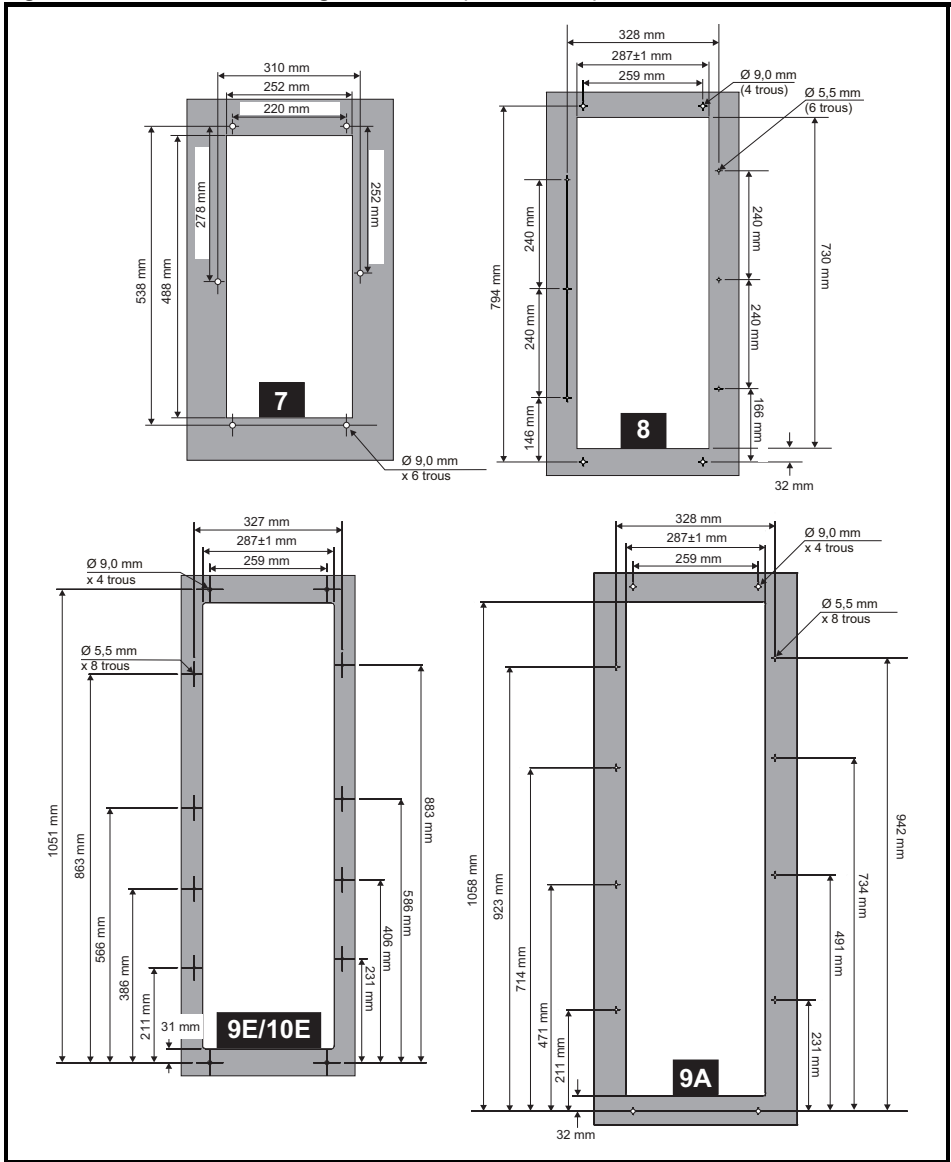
Dimensions montage en surface (tailles 7 à 10)
